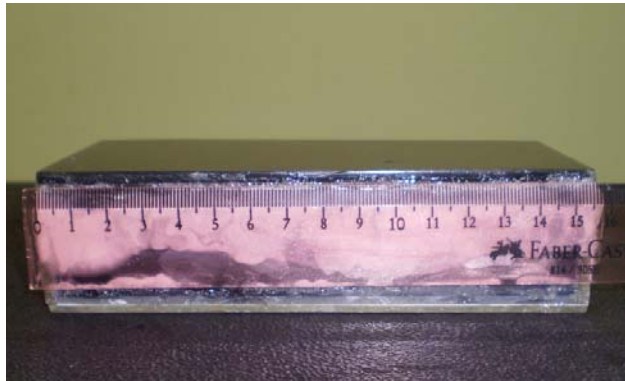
Escalerilla patrón marca KRAUTKRAMER
